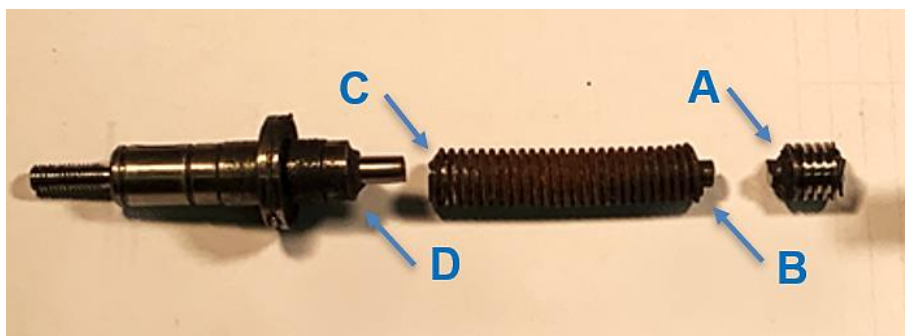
vista d'assieme dei diversi spezzoni dell'*acme screw* oggetto dell'indagine.
